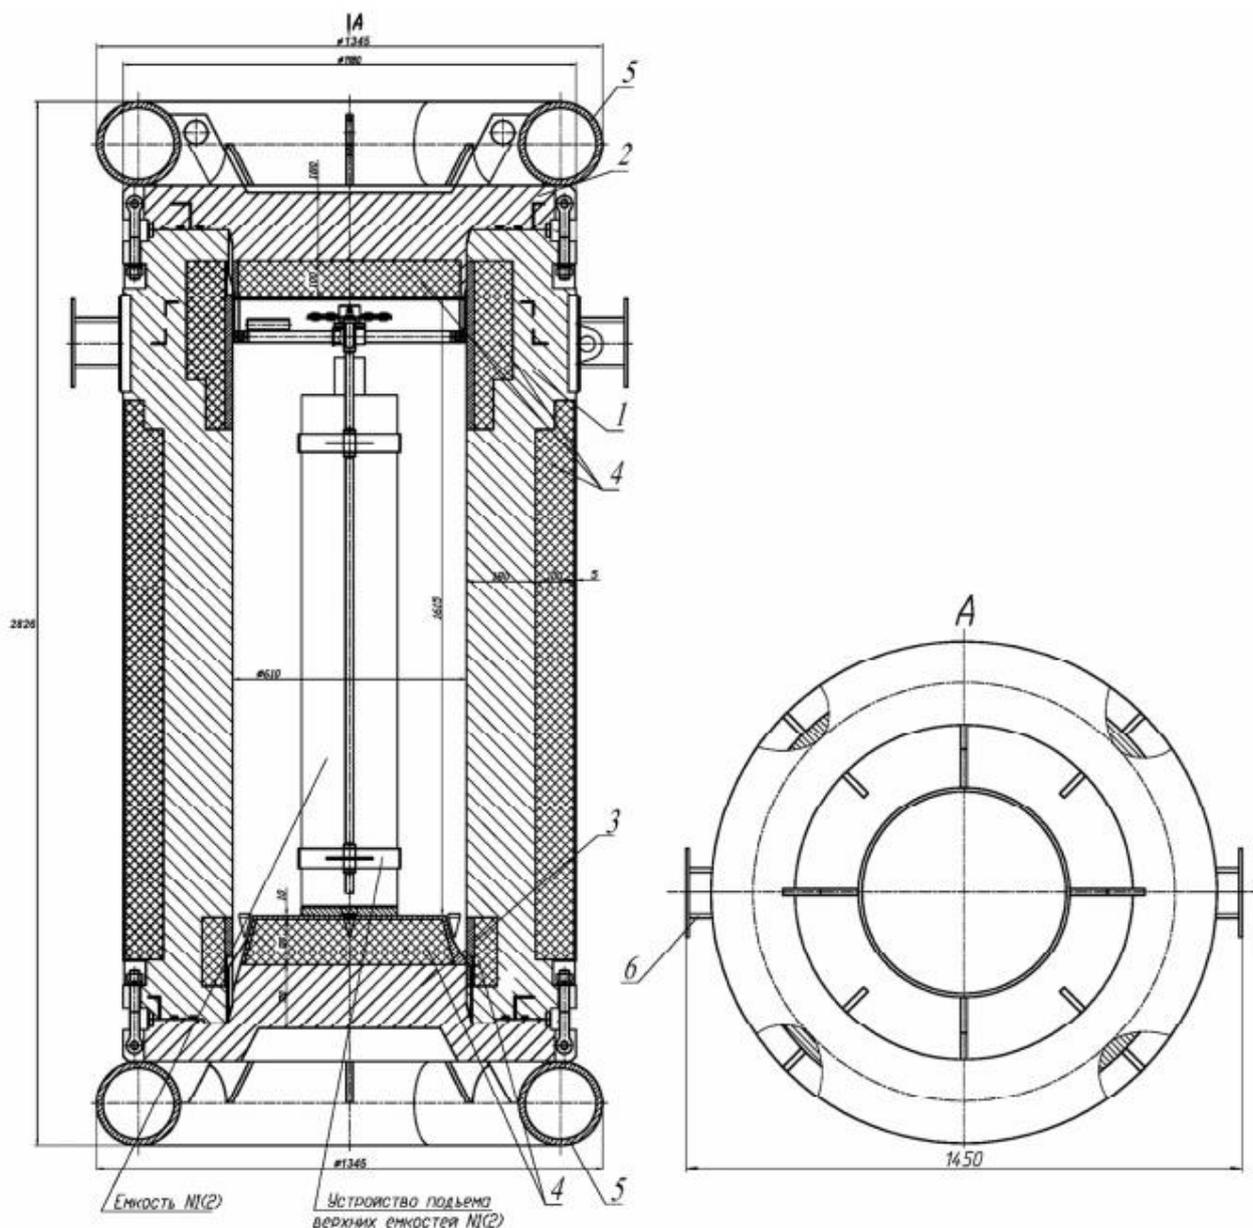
,б. Разрез ТУК: 1 – корпус; 2 – крышка верхняя; 3 – крышка нижняя; 4 – защита нейтронная; 5 – амортизатор; 6 – цапфа
